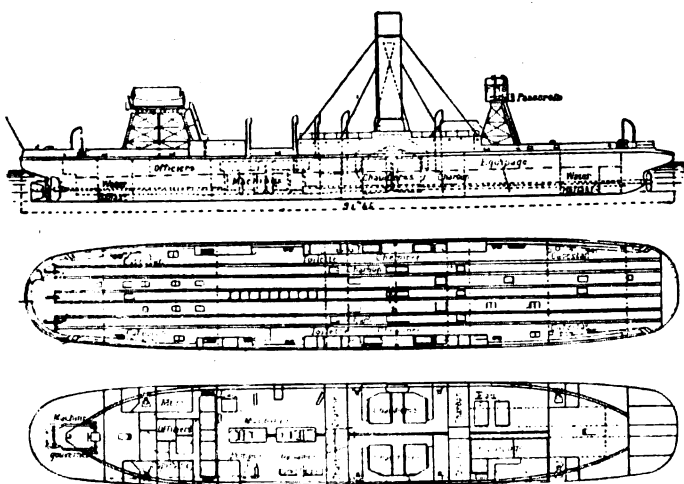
Alzato, pianta e sezione del ferry-boats rompighiaccio Scozia II.
